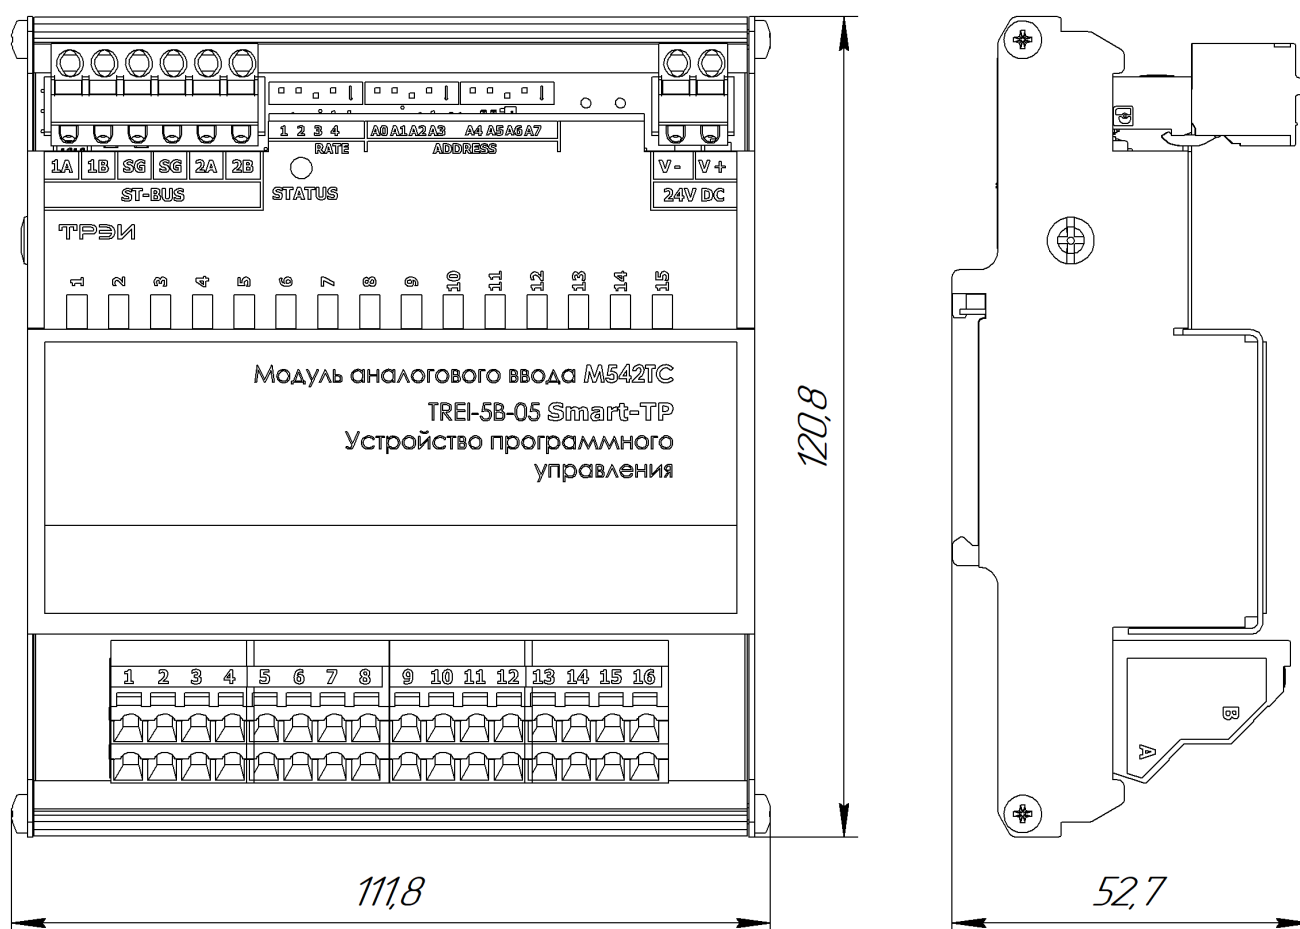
Чертеж общего вида M542TC с указанием габаритных и присоединительных размеров
